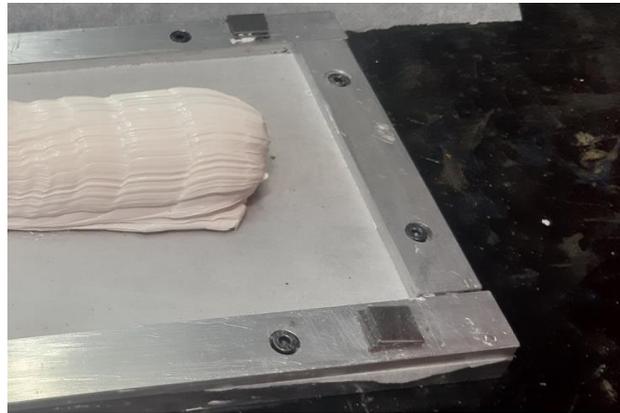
Adhesivo aplicado en el molde antes de extenderlo
